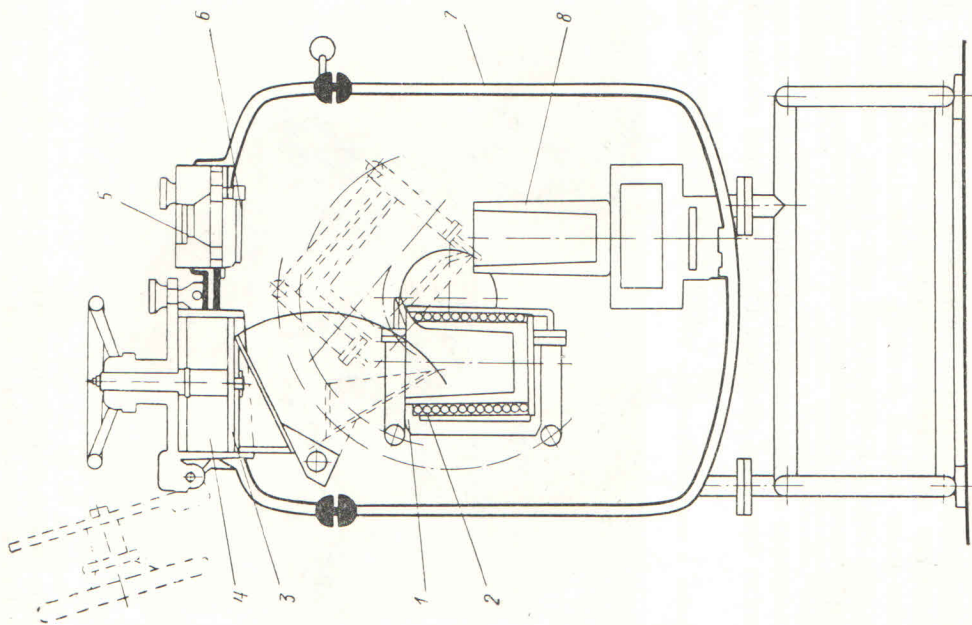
Схема вакуумной индукционной печи с вертикальным корпусом:
